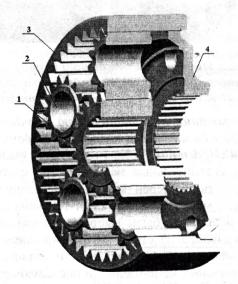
Планетарная колесная передача автомобит МАЗ. 1 — ведущая шестерня; 2 — сателлит; 3 — ведомая шестерня; 4 — ступица
